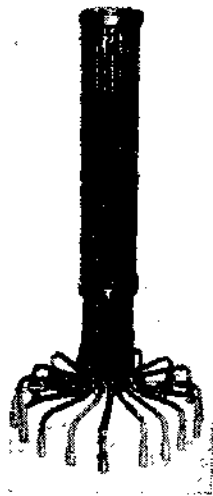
Трубчатый холодный тигель для наплавки слитка в вакуумной печи
